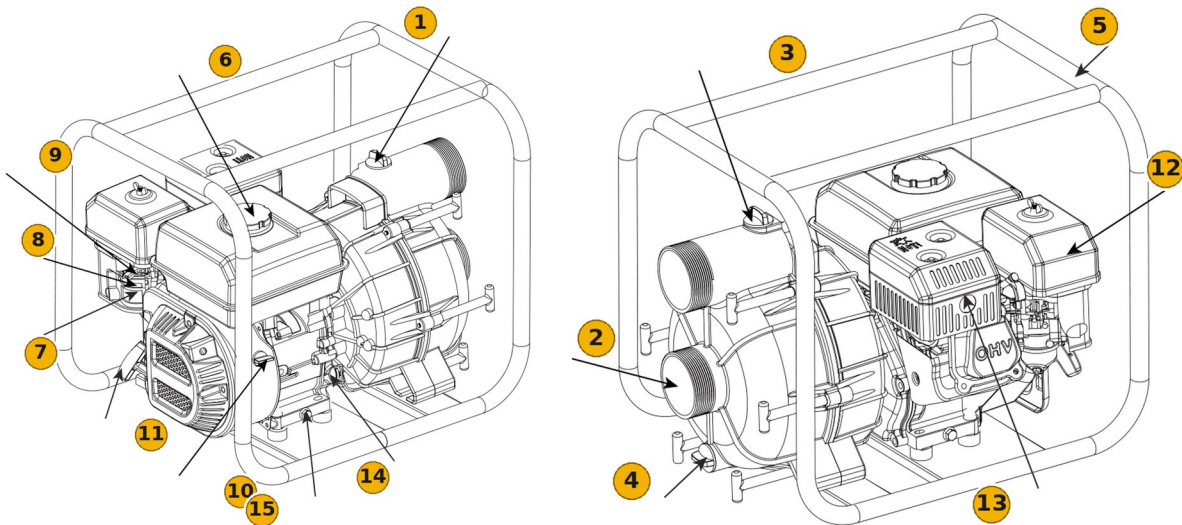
Motobombas SEMITRASH: vista del lado del motor y del lado de la bomba
